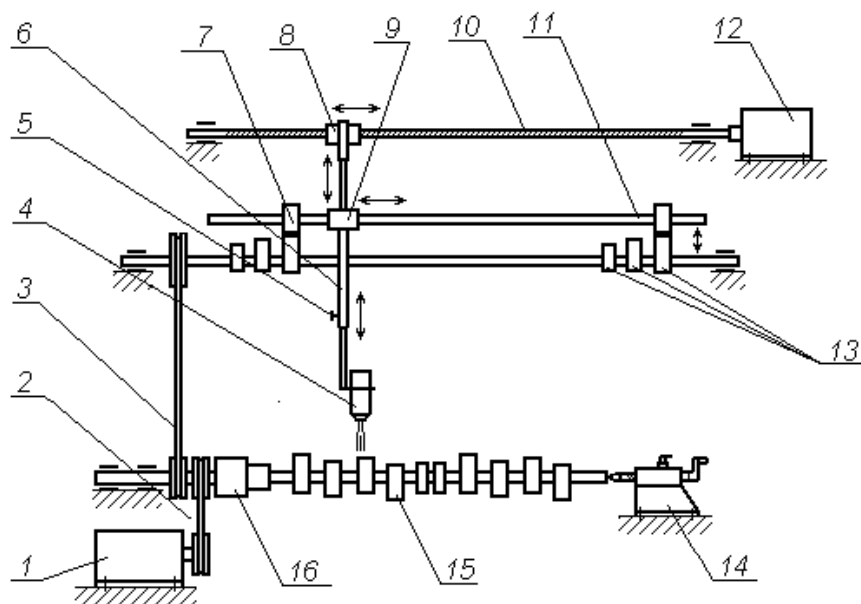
Устройство для напыления и оплавления покрытий на кулачках и опорных шейках распределительного вала
